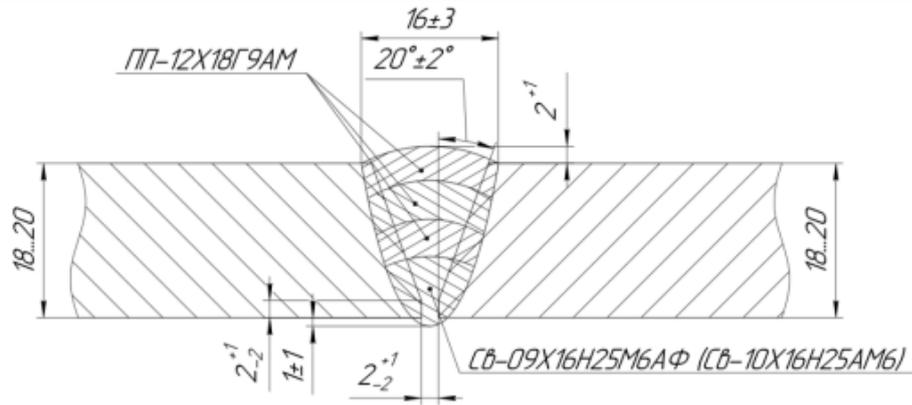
Конструктивні елементи підготовлених кромek зварюваних зразків та зварного шва
